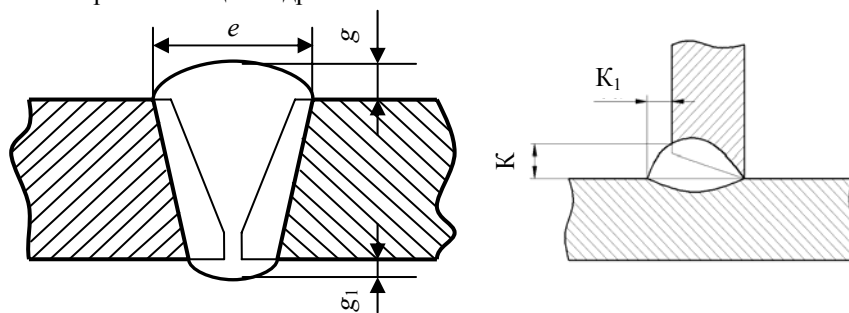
Схема замеров сварного шва и его дефектов
